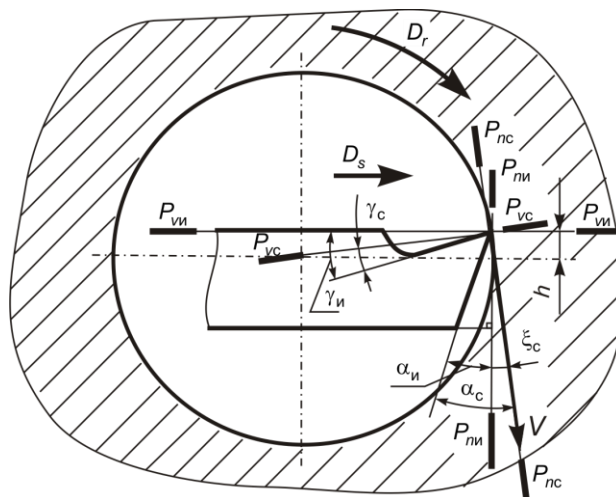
Особенности определения статических и инструментальных углов режущей части расточного резца при его установке выше оси заготовки
